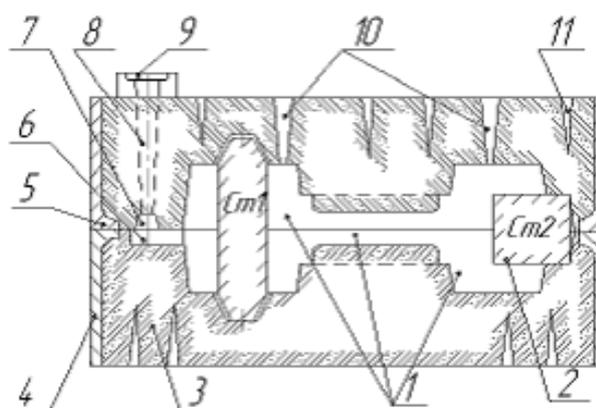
Литейная форма для получения отливки рычага: 1 – полость формы; 2 – стержни; 3 – формовочная смесь; 4 – нижняя опока; 5 – верхняя опока; 6–9 – литниковая система; 10 – выпоры; 11 – газоканалы.
